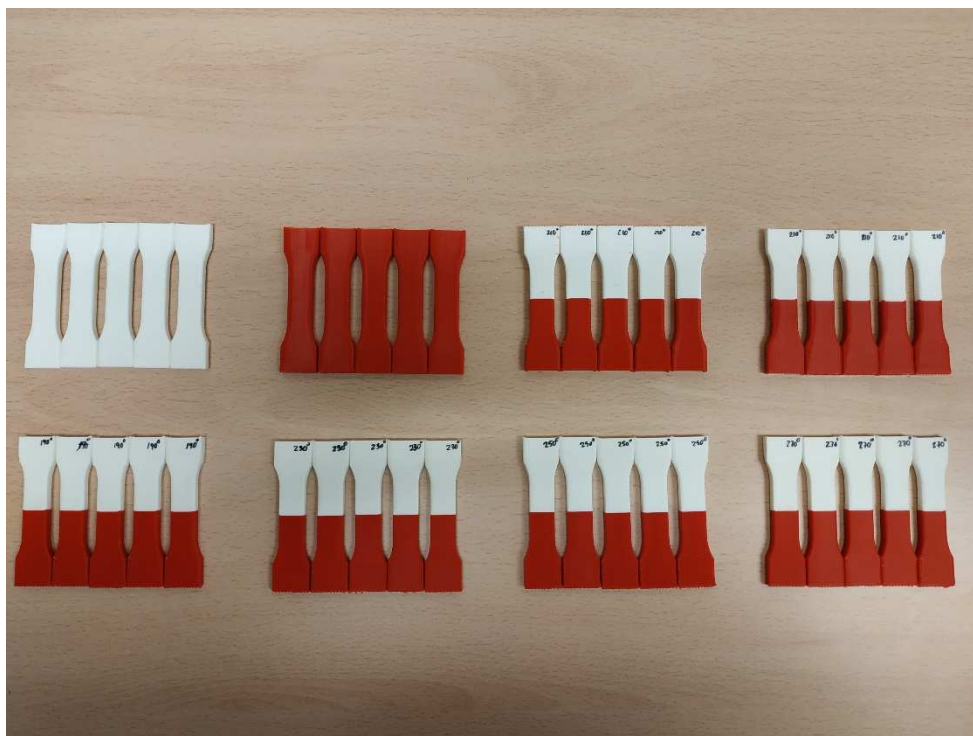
Detalle de todas las probetas para el ensayo de tracción
